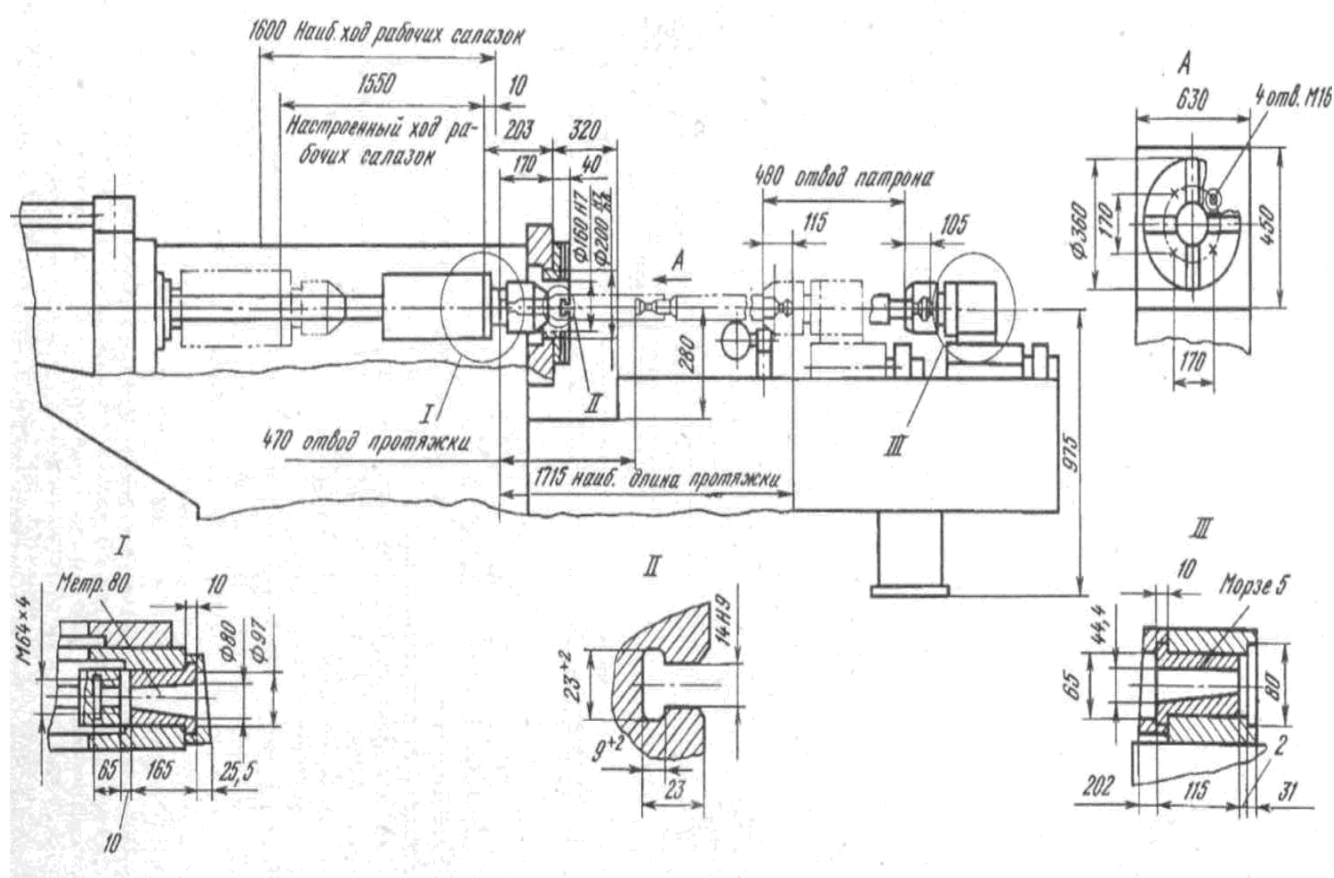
Схема наладки и присоединительные размеры горизонтального протяжного полуавтомата.
